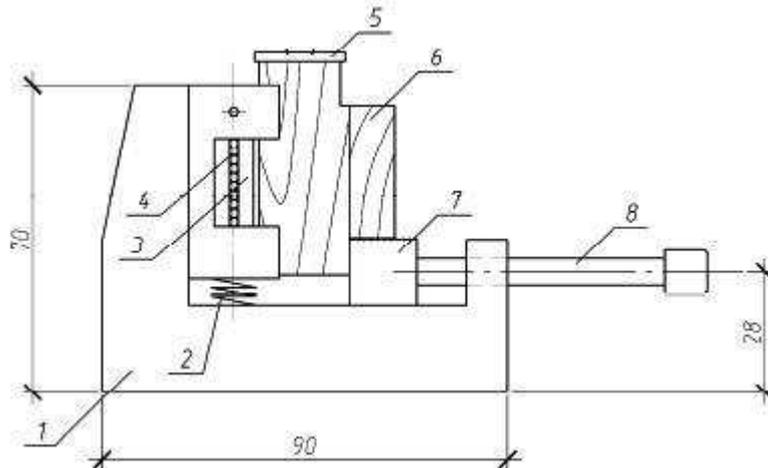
Приспособление для испытаний на скалывание [5]
